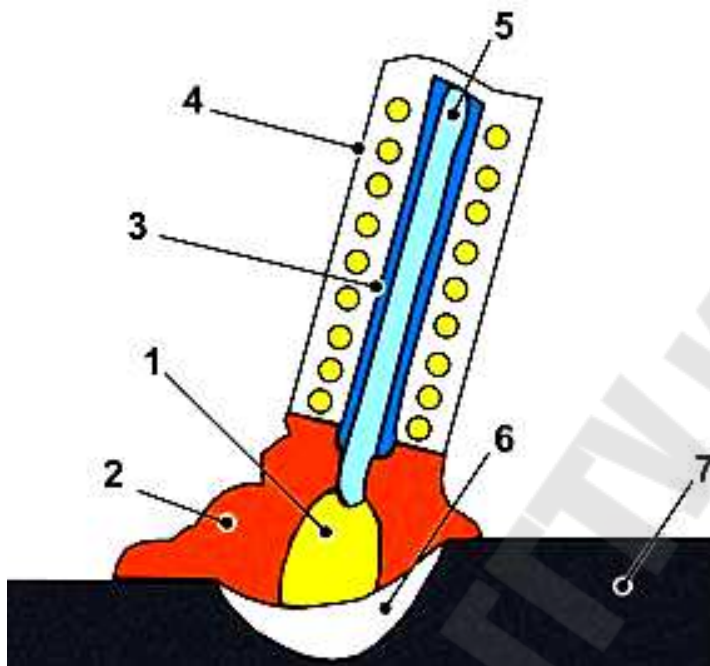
Схема электродуговой сварки: 1 – сварочная дуга; 2 – газовая защита; 3 – зажим электрода; 4 – сопло; 5 – тугоплавкий электрод; 6 – сварочная ванна; 7 – металл шва
